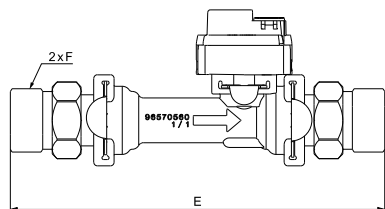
Abmessungen des Sensors VFS 2-40 l/min (mit Adaptern)
